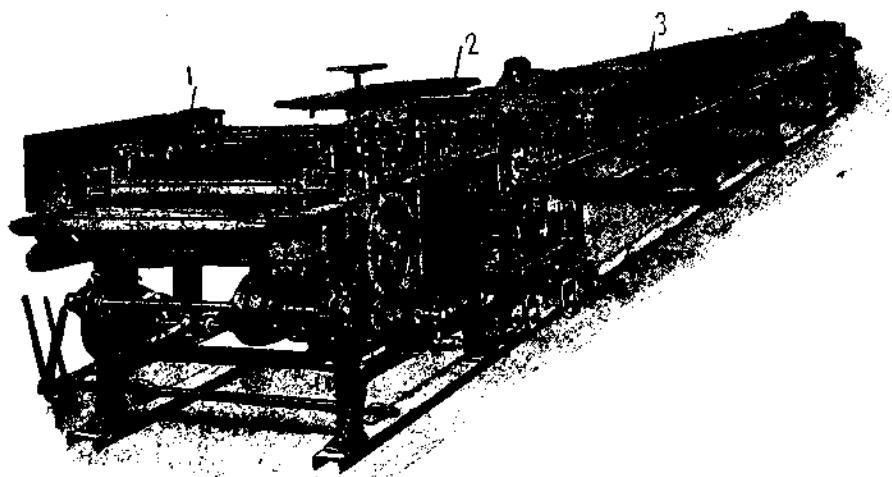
Моечно-подслойный агрегат для фотопластиинок: 1—круглые щетки, 2—место для каскада, 3—сушильный ковер
